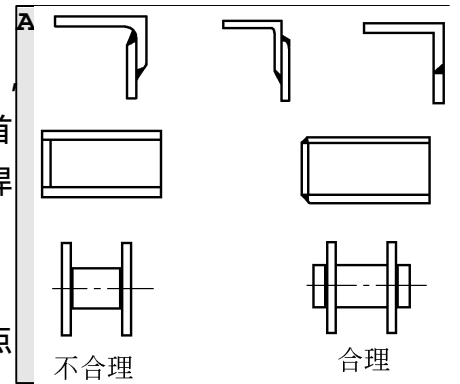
5 .1 焊条电弧焊焊缝位置
